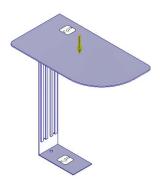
Restricciones aplicadas en Estudio 2: Mesa
